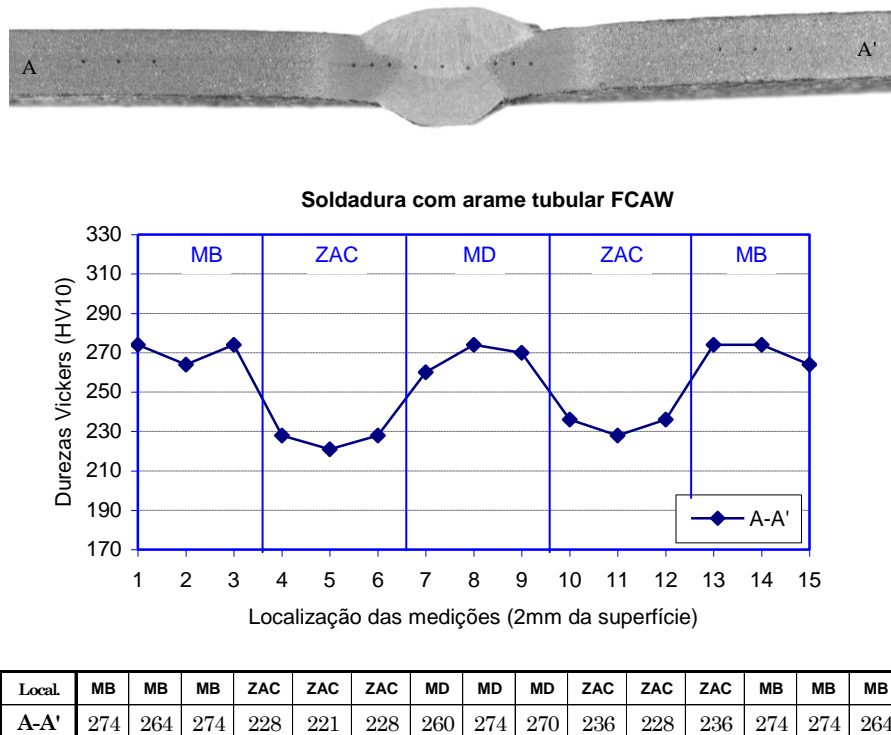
Perfil de dureza para a soldadura com arame tubular (FCAW)
